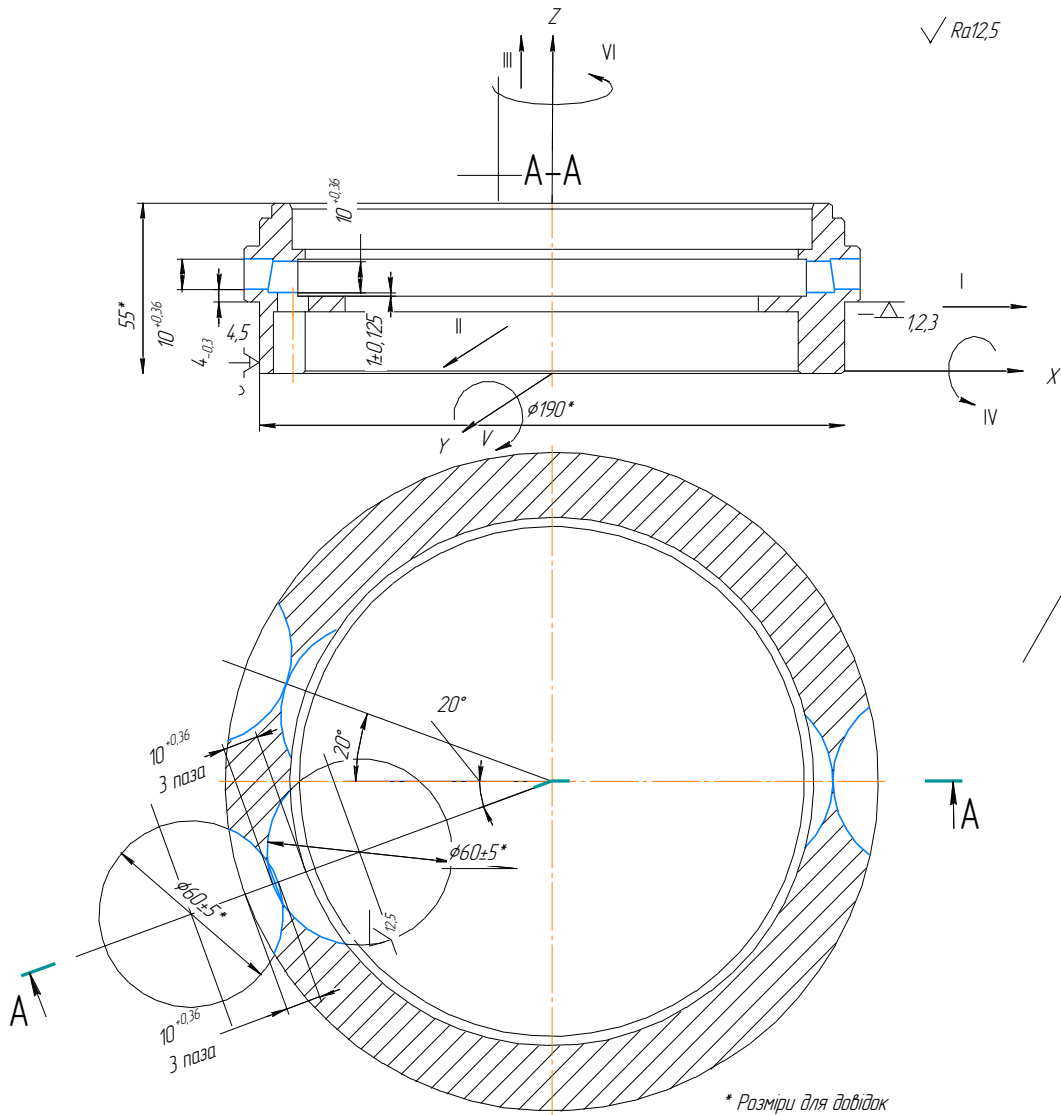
Альтернативна схема базування на фрезерній операції 040
